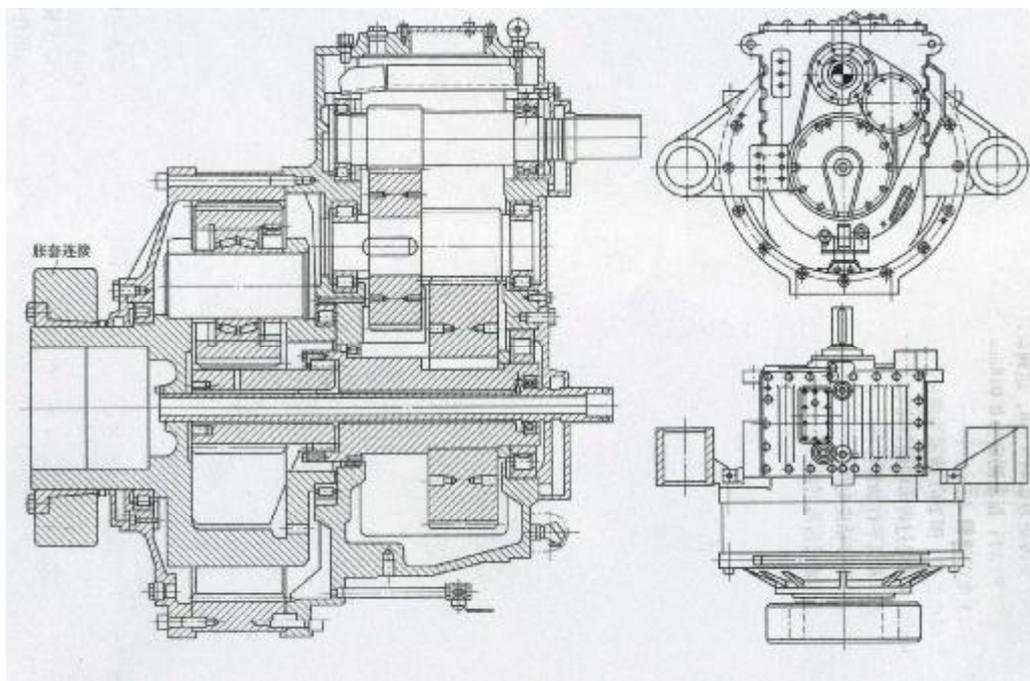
一级行星和两级平行轴圆柱齿轮传动齿轮箱（风电齿轮箱）
